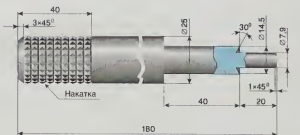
Оправка для запрессовки (выпрессовки) штатной втулки клапана.
